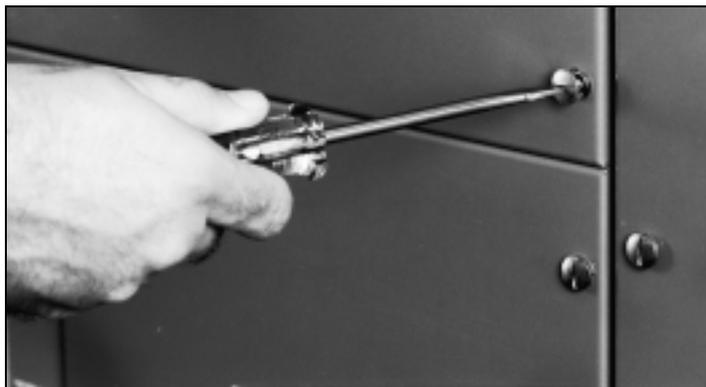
Desserrage des vis imperdables d'un quart de tour
